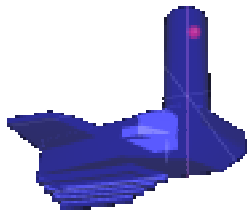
Visualización 3D de la posición en la que se encuentra el defecto en la pieza inspeccionada
